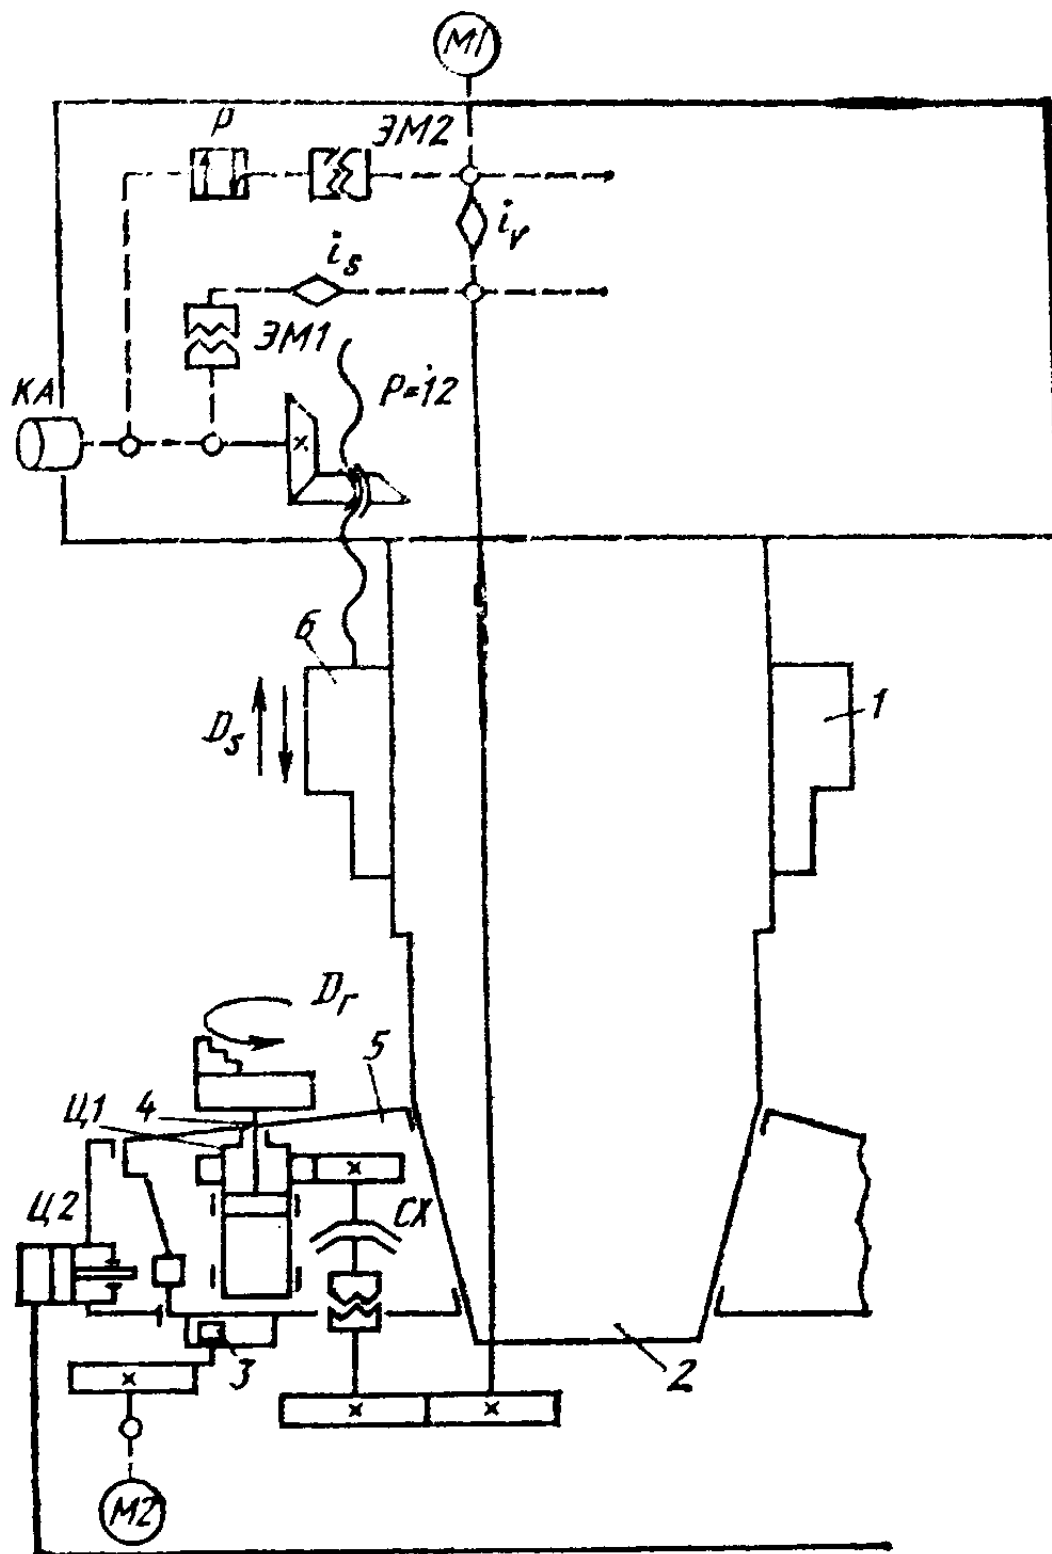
Вертикальный токарный восьмишпиндельный полуавтомат 1К282
